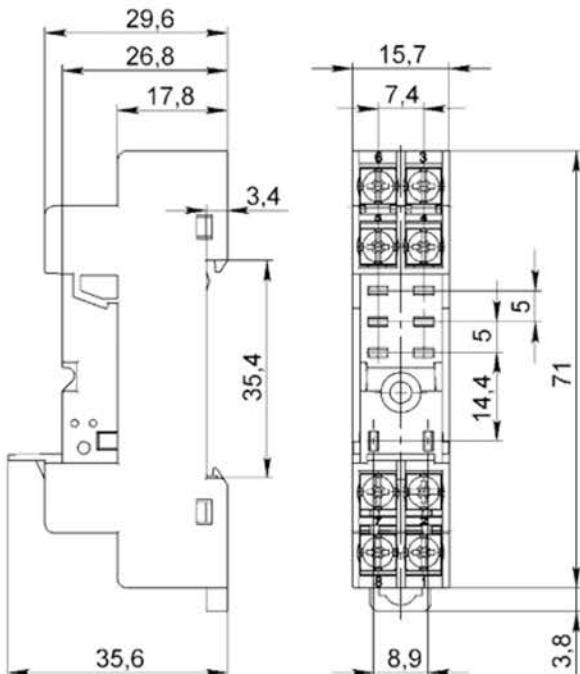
Габаритные, установочные, присоединительные размеры розеток OptiRel G RR 97-72-230-10-V
